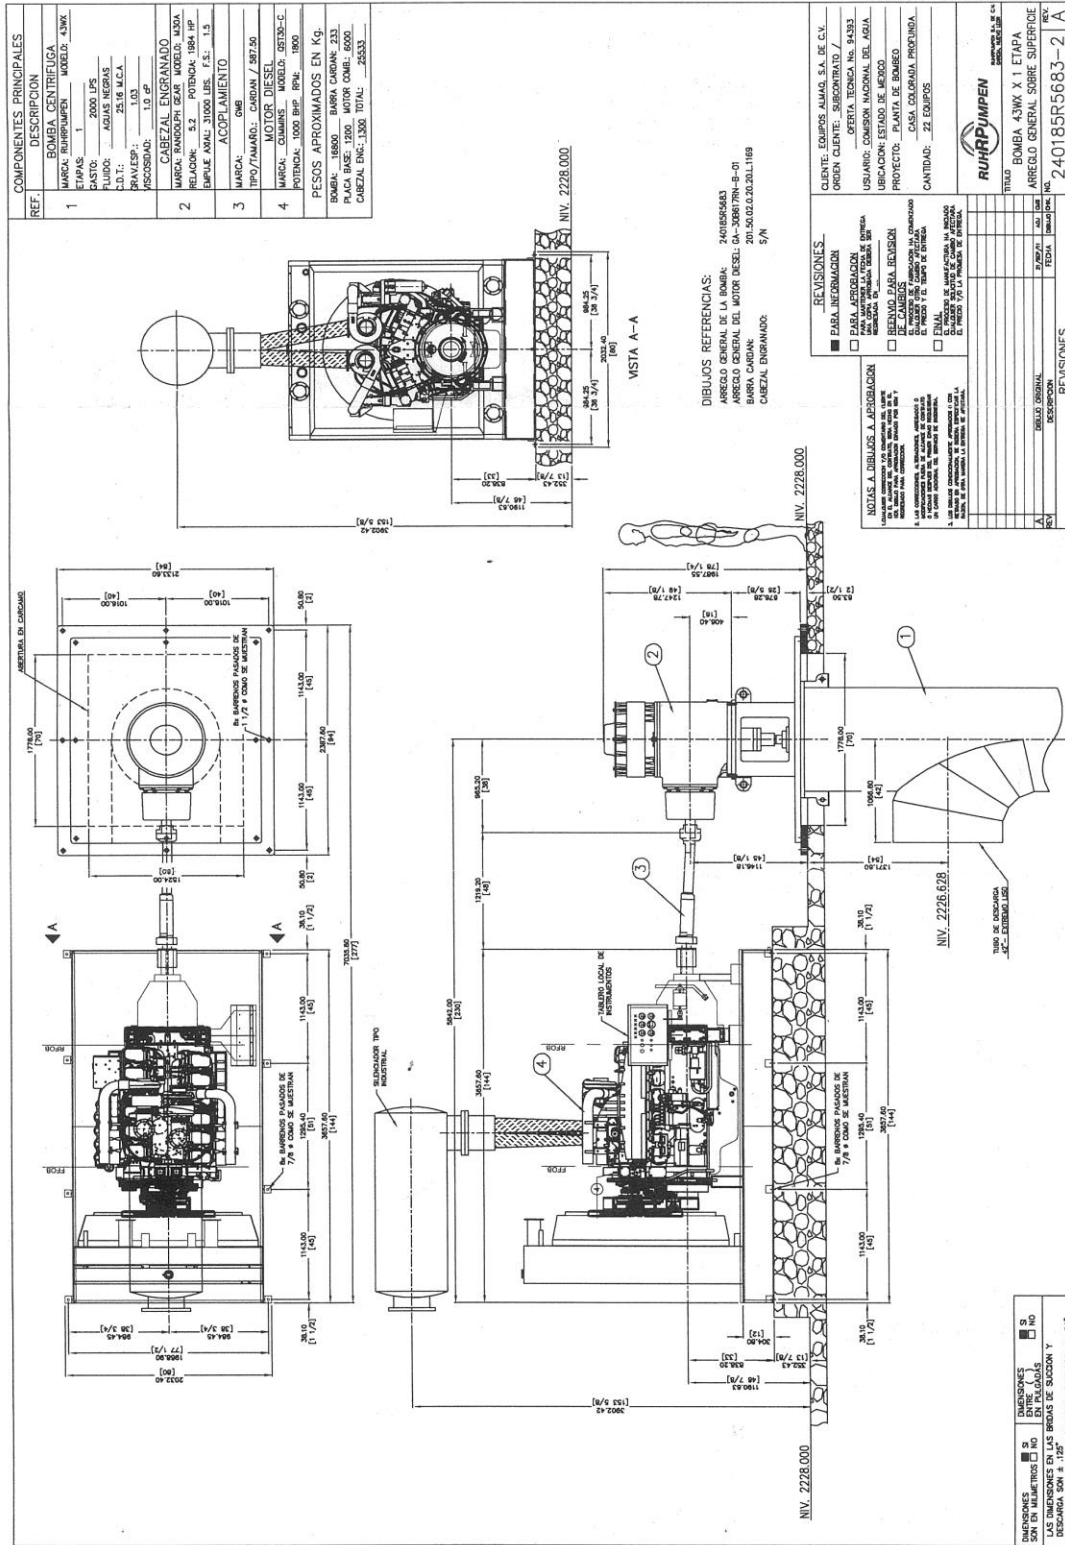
Dimensiones Generales del Grupo Motor Diesel-Flecha Cardan-Cabezal Engranado
